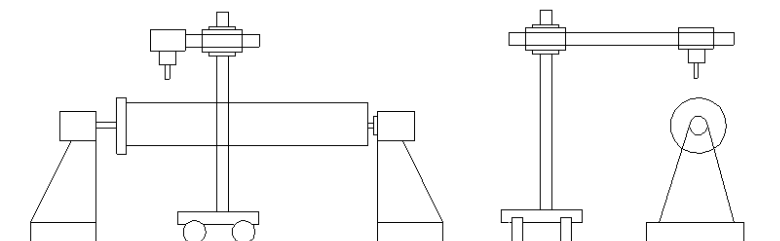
Установка самоходного сварочного аппарата
